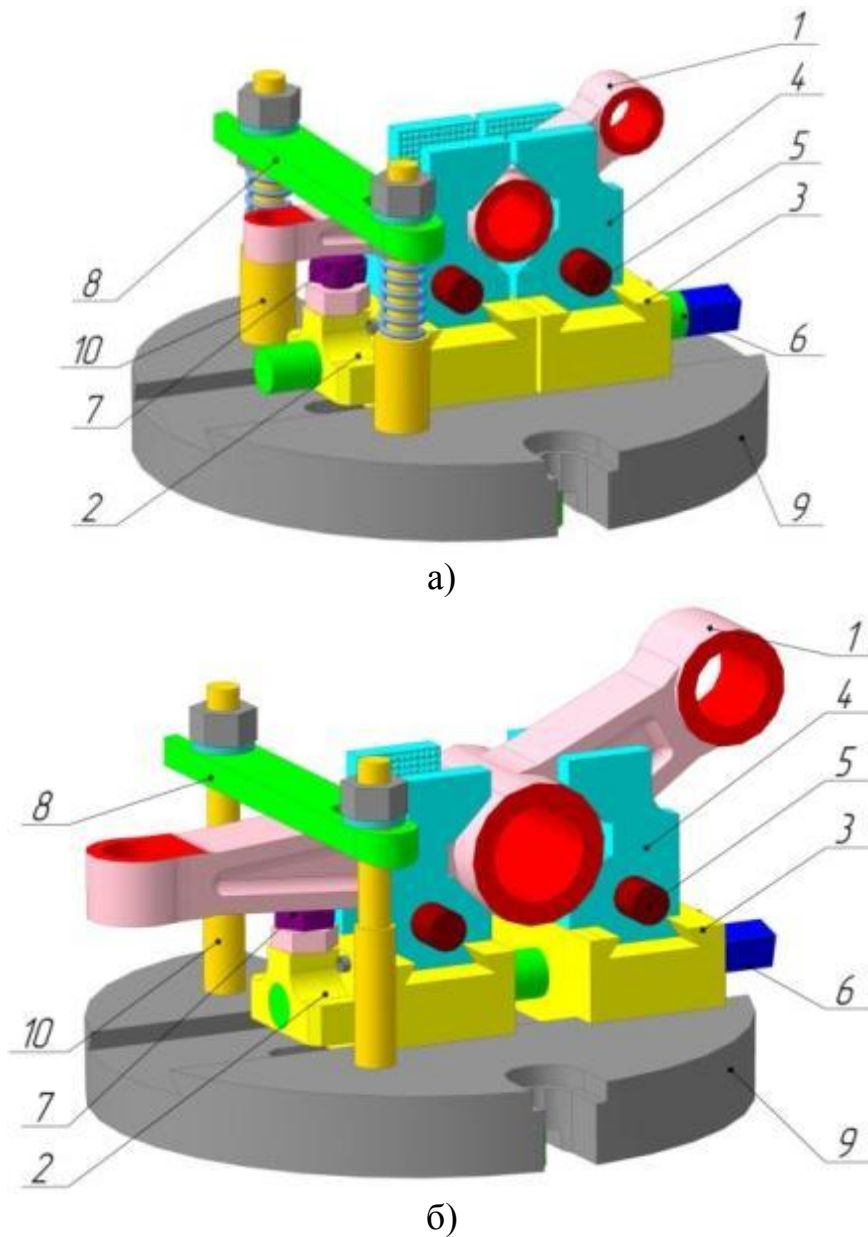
Переналаджуваний установлювально-затискний модуль для обробки деталей типу важелів:
